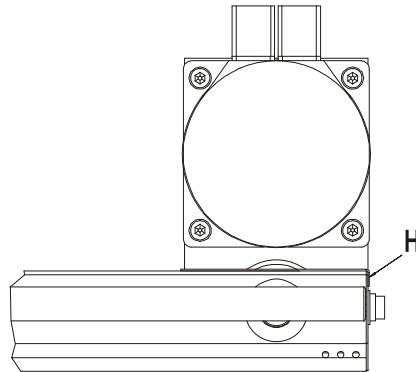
Riemengetriebe, Ansicht motorseitig
